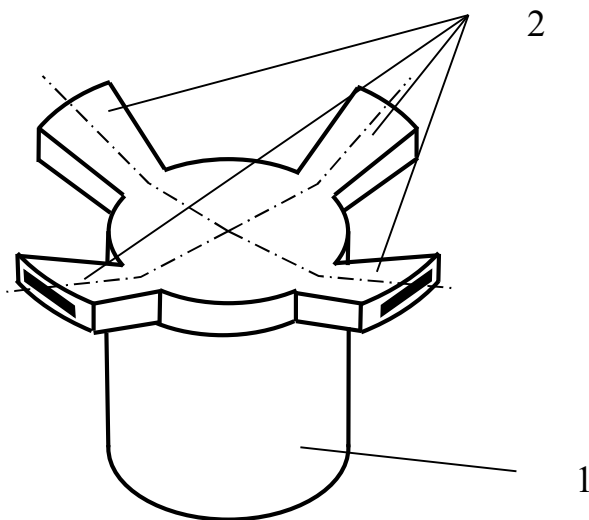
Загальний вигляд пожежного монітора: 1 – корпус; 2 – насадки
